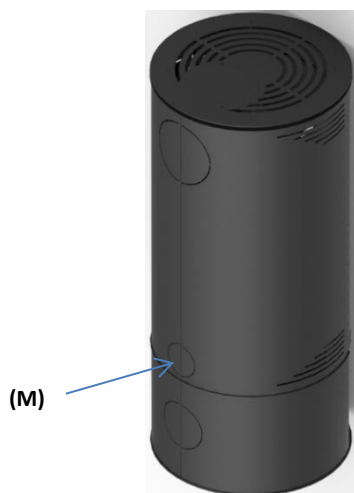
Vista posteriore dell'apparecchiatura, sezione (M) da eliminare per la presa d'aria esterna
